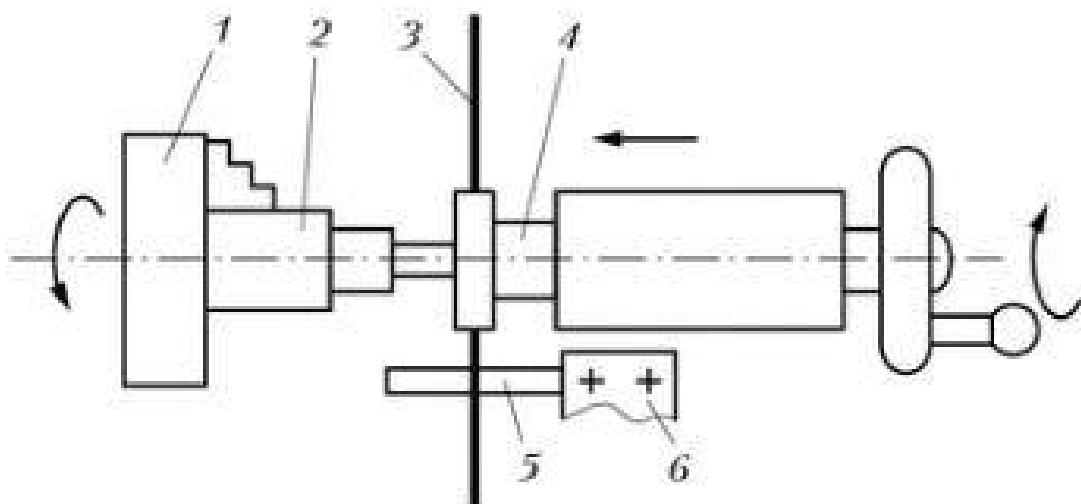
Нарезание резьбы плашкой на токарно-винторезном станке:
